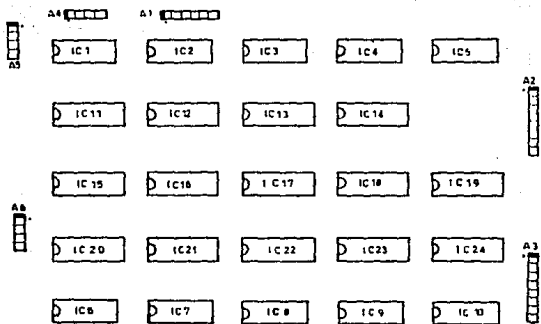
Ensamble de componentes tarjeta FDP-A.
